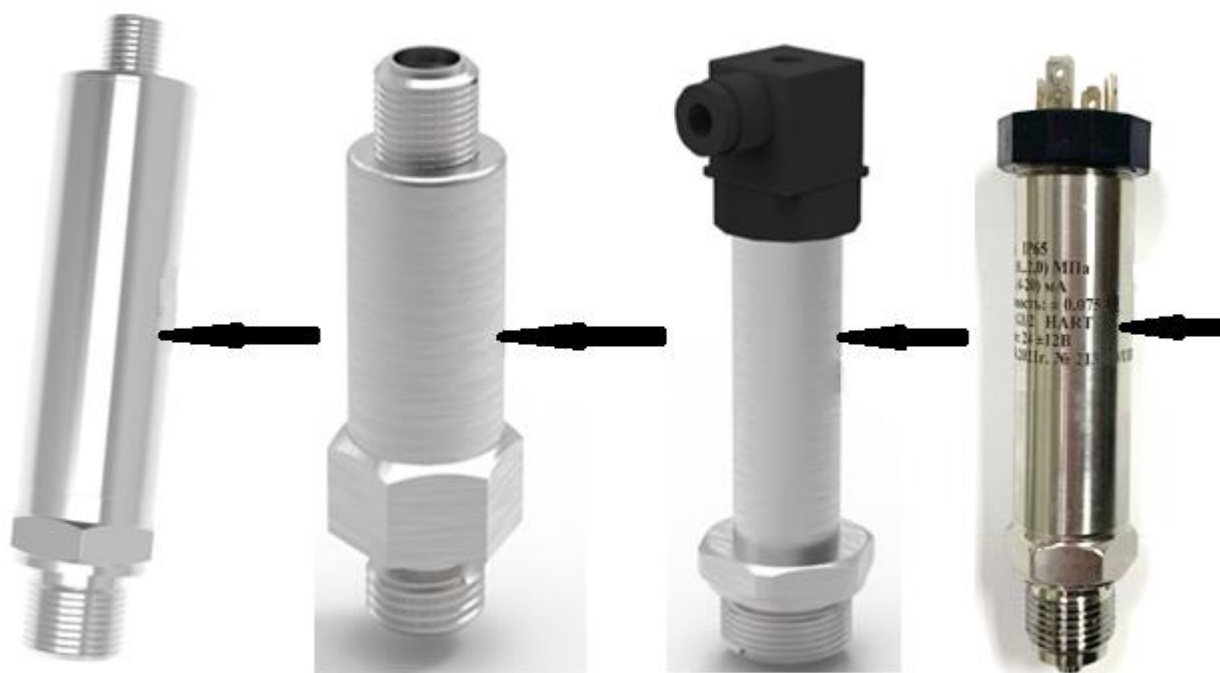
Общий вид датчиков ИД-Qк и ИД-Qм с исполнением корпуса Tr, Tr1
